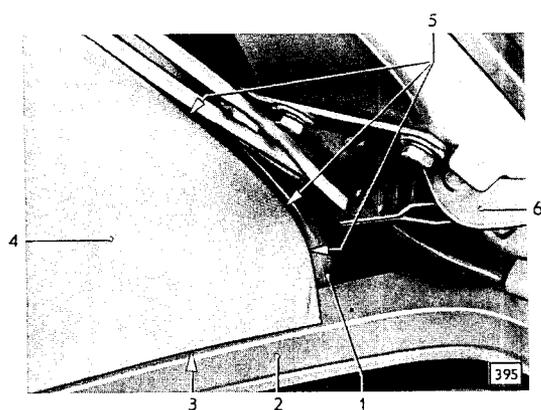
Himmelbefestigung am hinteren Dachspiegel – Caravan
